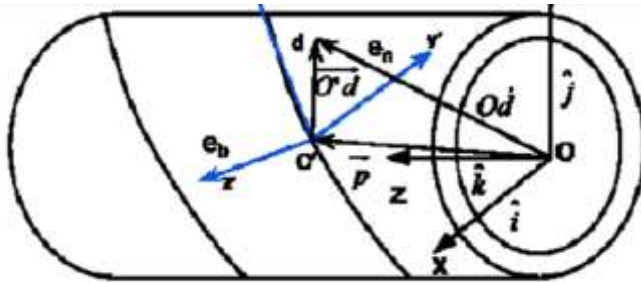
Dimensiones globales de soldadura helicoidal en el tubo (12).
